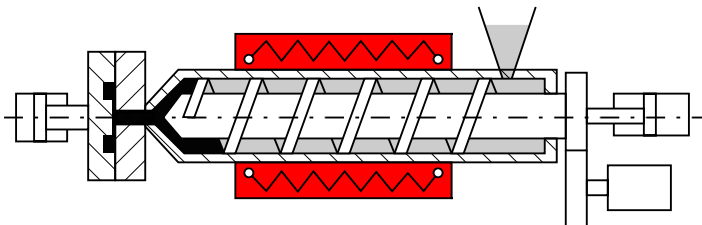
rfZ) Schnecke (rechts) und Werkzeug (links) einer Spritzgiessmaschine
